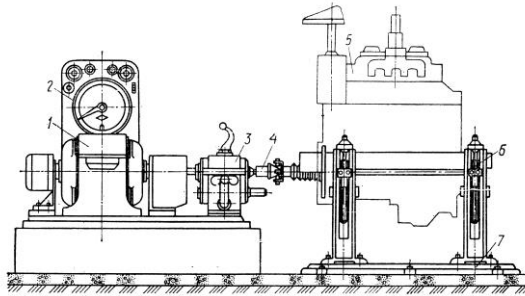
Стенд для обкатки двигунів: 1 – електродвигун; 2 – ваговий механізм; 3 – редуктор; 4 – муфта; 5 – двигун; 6 – регульовані стійки; 7 – фундаментна плита
